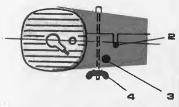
Кожух карбюратора; 1 — резиновый клапан; 2 — паз для троса газа; 3 — отверстие для шланга; 4 — стяжной болт.
